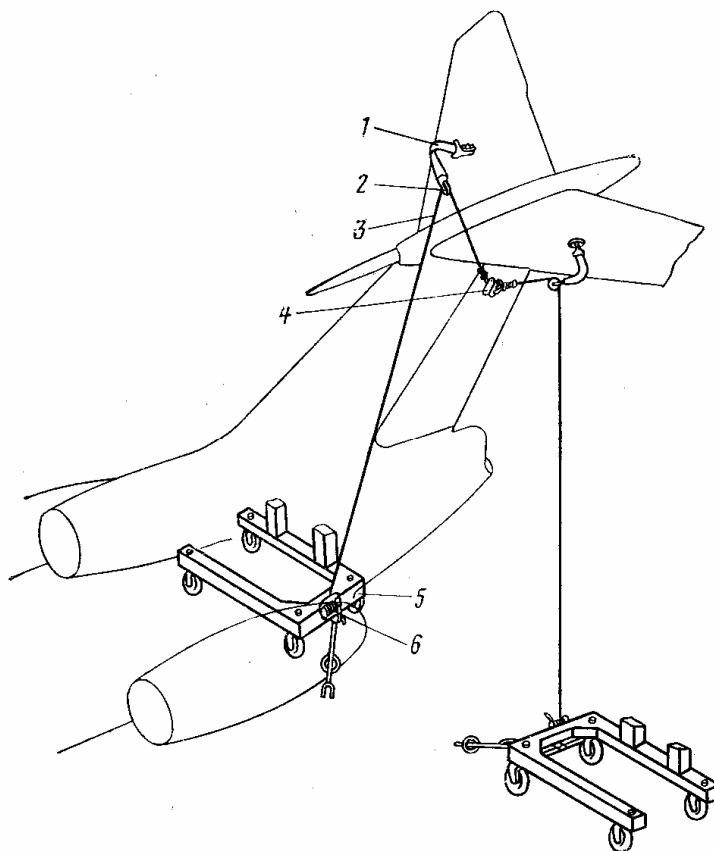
Приспособление 154.80.9934.000 для монтажа руля направления:
